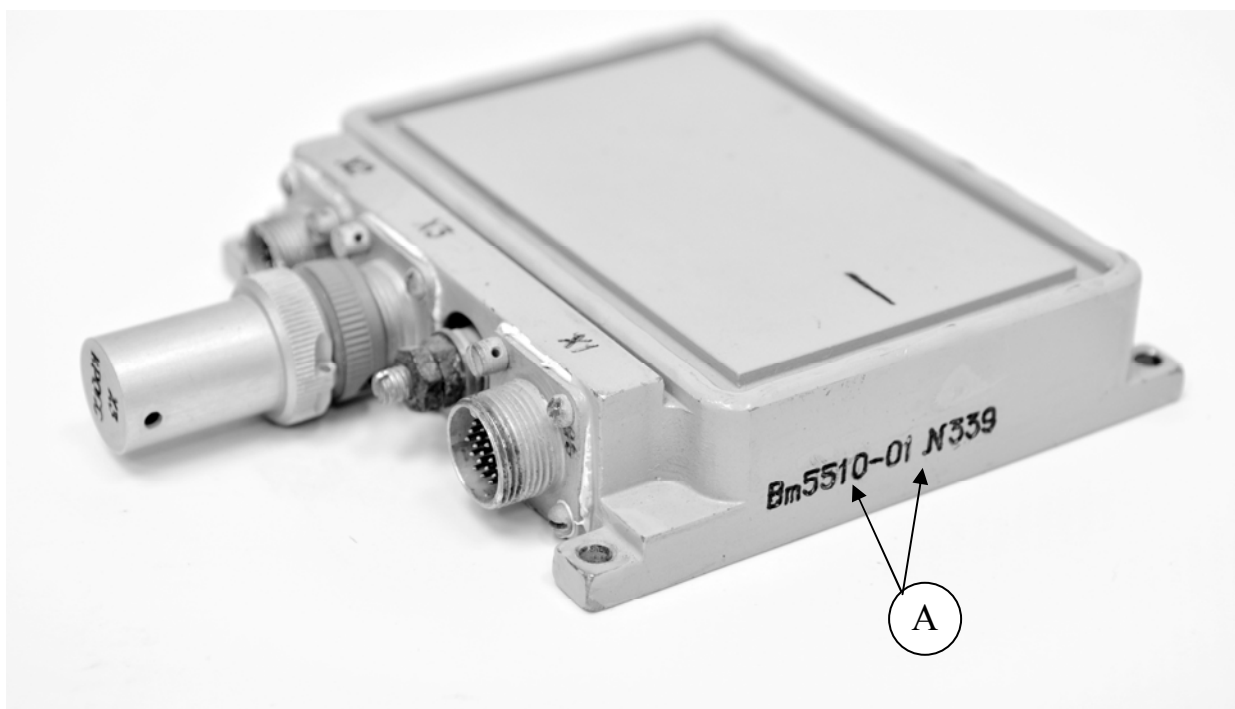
Схема обозначения мест маркировки и заводского номера
